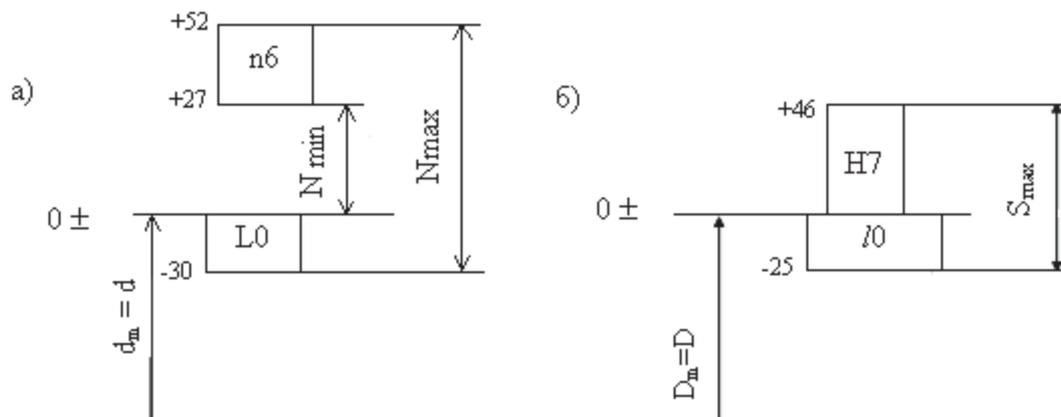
Поля допусков деталей подшипникового соединения:
